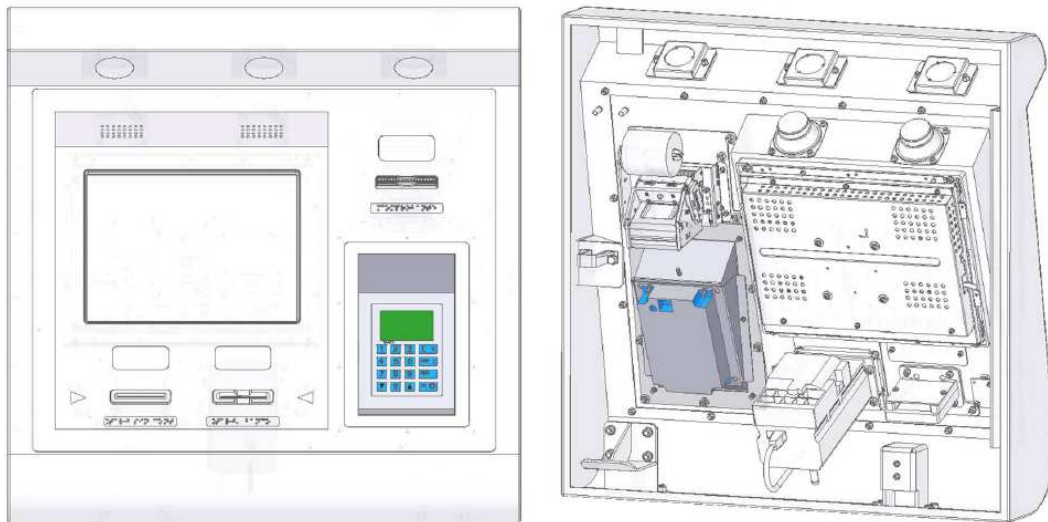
Elementos del conjunto PIN-PAD a retirar (METTA).
